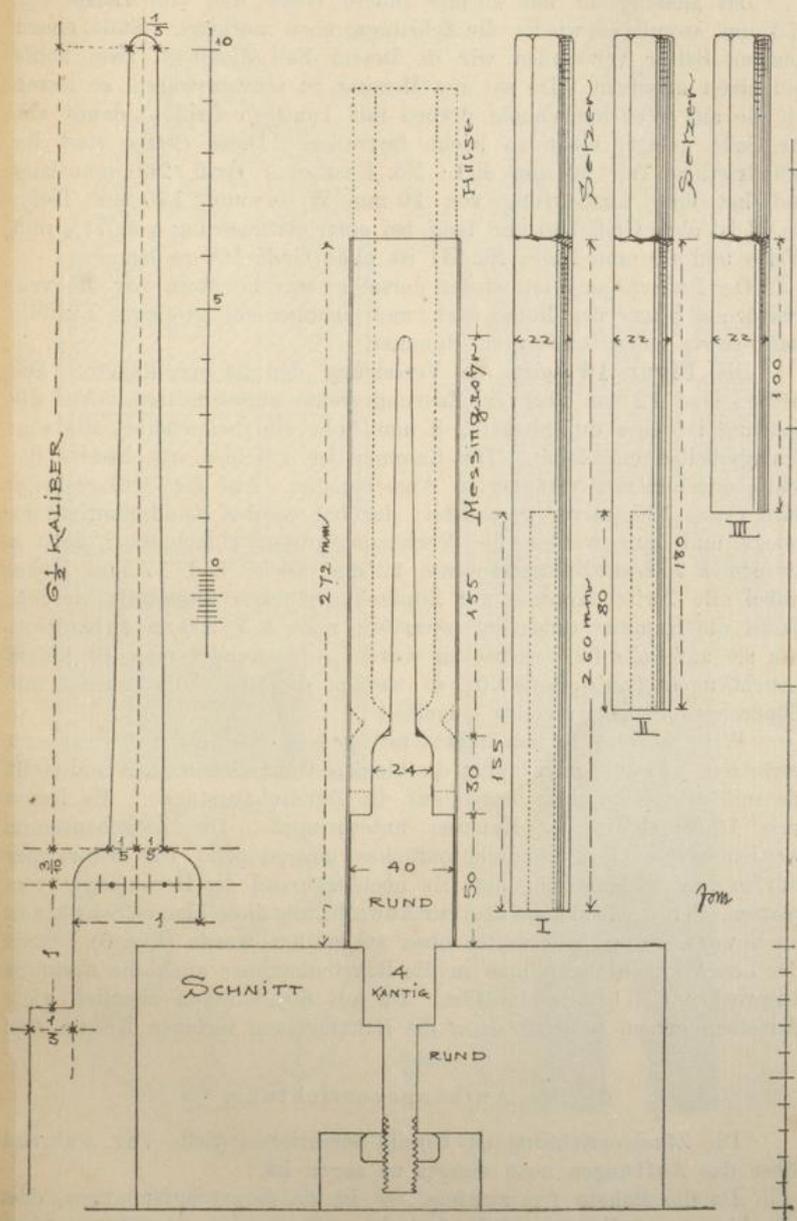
Untersatz und Setzer für die 24 mm-Rakete.
